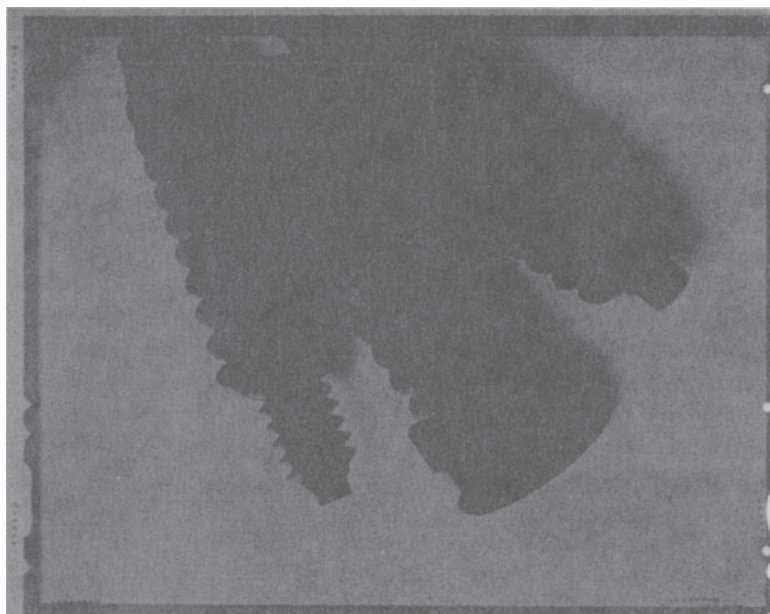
Полые изделия из ТПВ: автомобильные детали — зубчатая рейка и зубчатый валик
